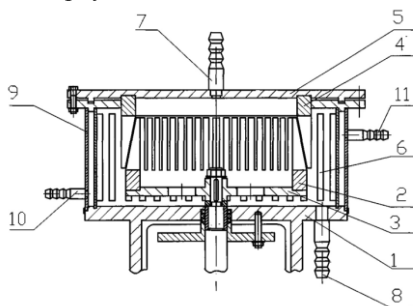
Роторно-пульсационный экстрактор с направляющими лопастями: 1 – корпус; 2 – ротор; 3 – отверстия; 4 – статор; 5 – крышка; 6 – лопасти; 7, 8 – патрубки; 9 – тепловая рубашка; 10, 11 – патрубки тепловой рубашки
